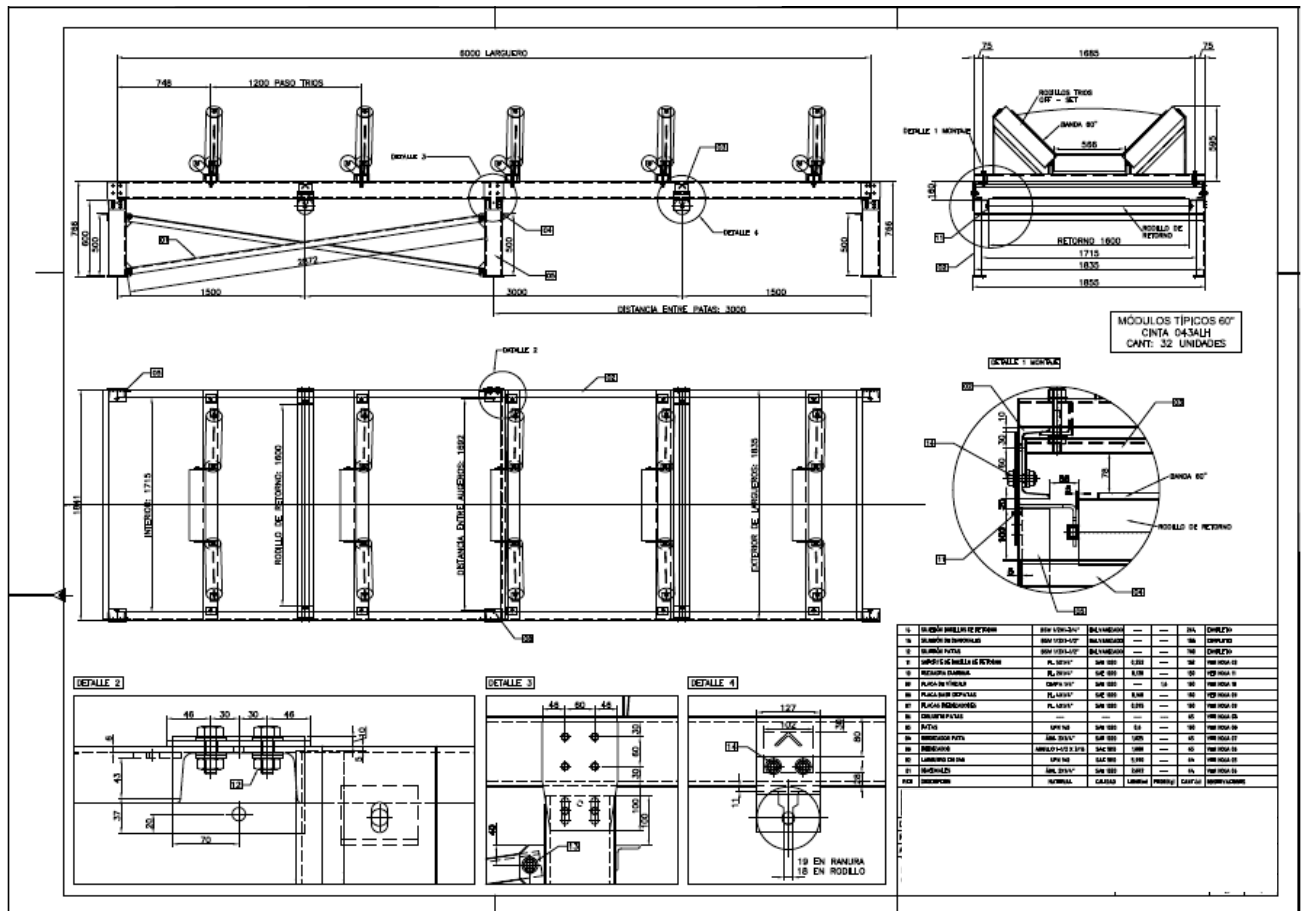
Imagen de plano típico para banda 60" y tríos 45°
